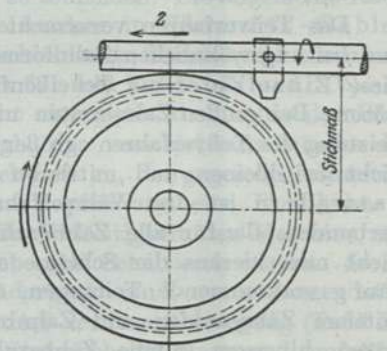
Fräsen der Schneckenräder mit Schlagmesser.
